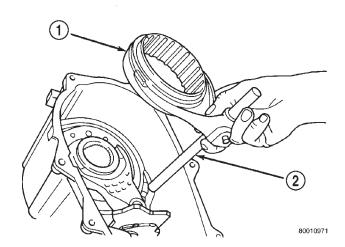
Ensamblaje de la horquilla y el manguito de modo
